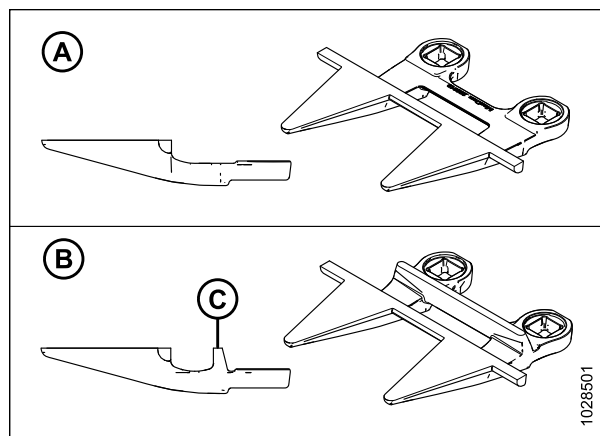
Концевой противорежущий палец и укороченный противорежущий палец
